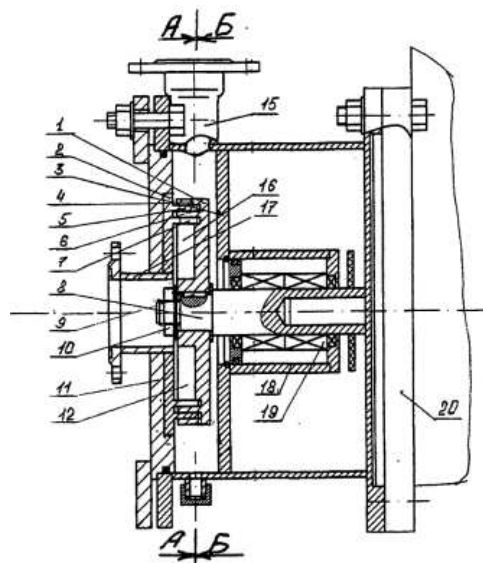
Конструкція РПА з можливістю реверсивного обертання ротора: 1 – ротор; 2 – статор; 3 – корпус; 4, 5 – ряди шипів; 6, 7 – пази; 8 – привідний вал; 9, 10 – фіксуючі пристрої; 11 – кришка; 12 – вхідні лопатки; 13 – додаткові вхідні лопатки; 14 – вихідні лопатки; 15 – напірний патрубок; 16 – камера попереднього змішування; 17 – впускний патрубок; 18 – корпус підшипника; 19 – підшипниковий вузол; 20 – фіксуюча плита
